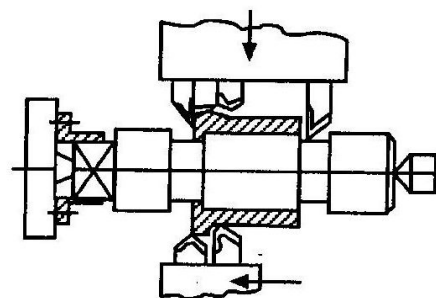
Налагодження токарного багаторізевого напівавтомата для обточування зовнішньої поверхні і підрізання торців
